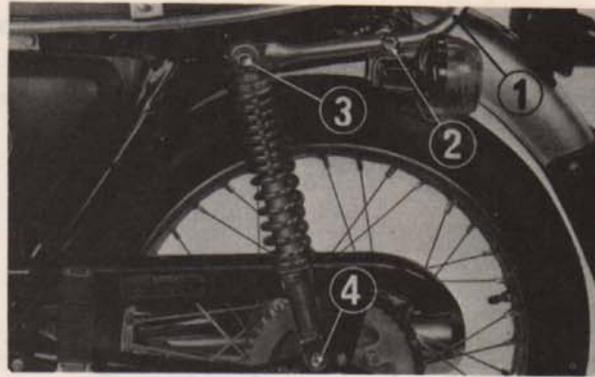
(1) Tube métallique de pare-chocs arrière
